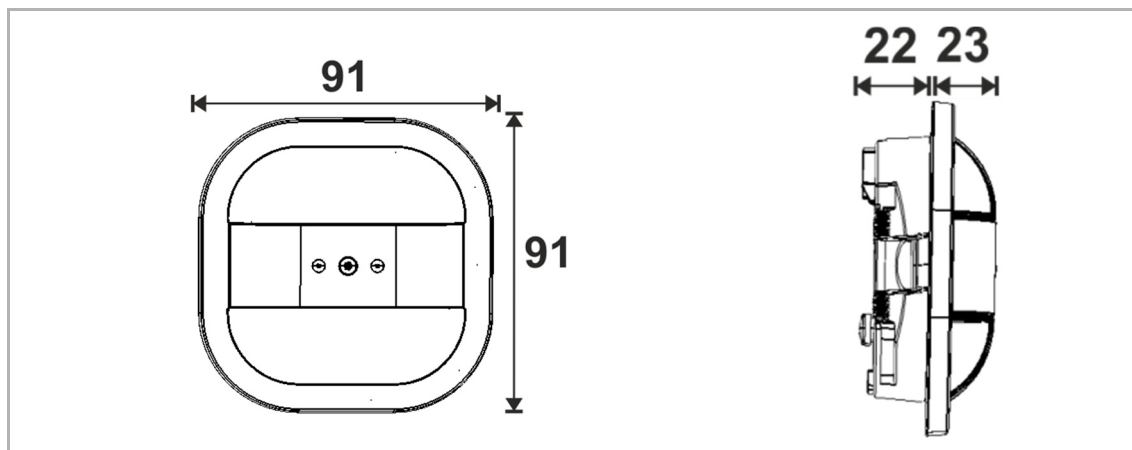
Dimensiones detector de presencia Busch KNX/Busch Premium KNX
